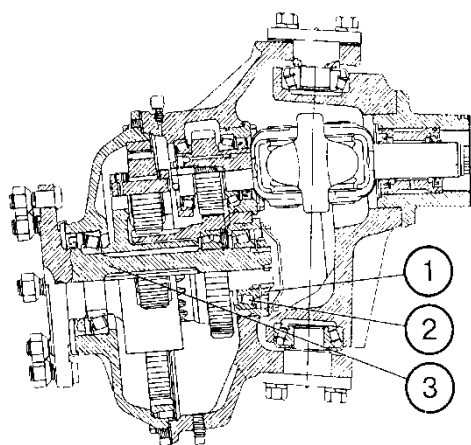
Проверка зазоров в подшипниках передних колес:
